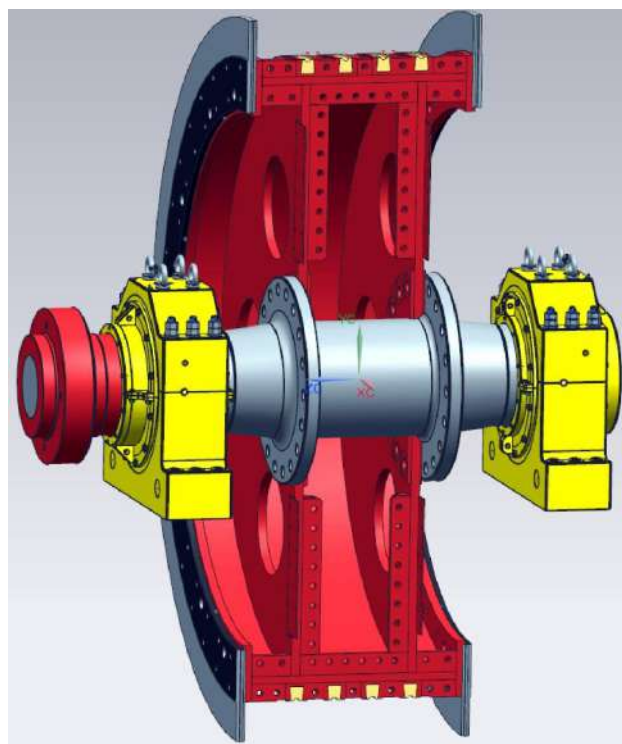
Конструктивная схема соединения коренного вала с барабаном канатоведущего шкива ШПМ
